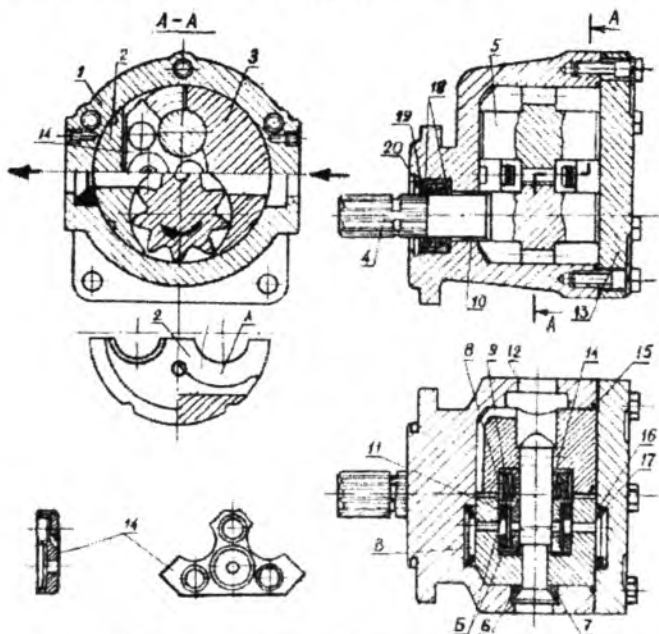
Односекционный шестеренный насос в круглом корпусе.
